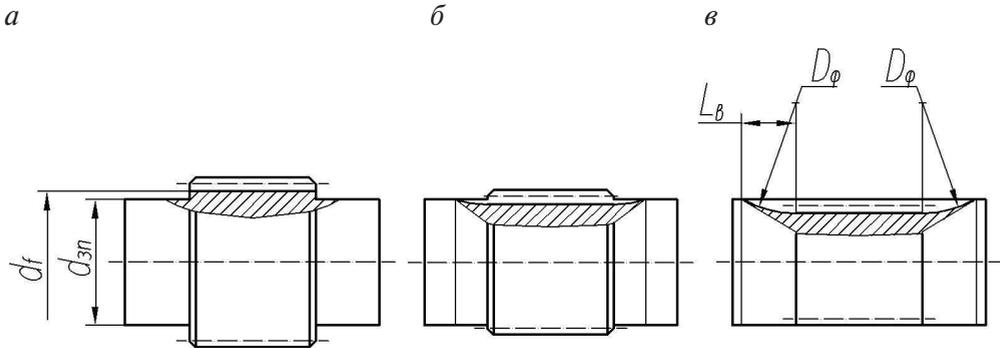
Конструкция вала-шестерни цилиндрической
